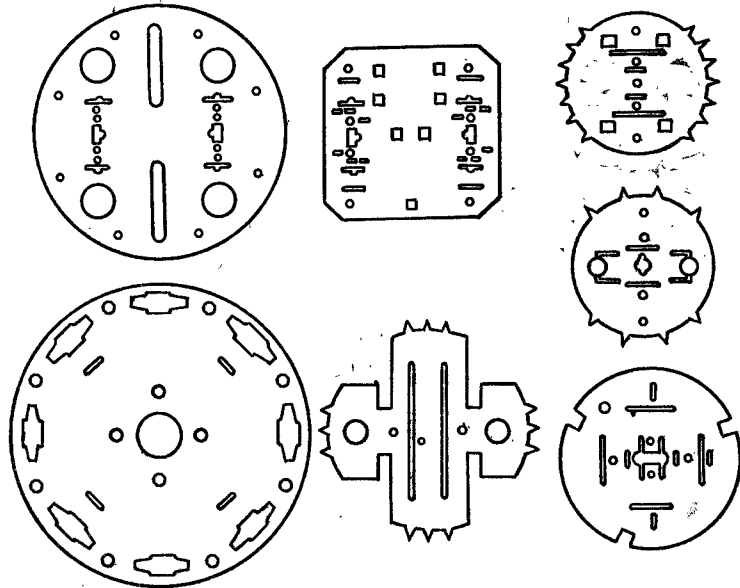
Слюдяные пластинки с точными размерами отверстий
